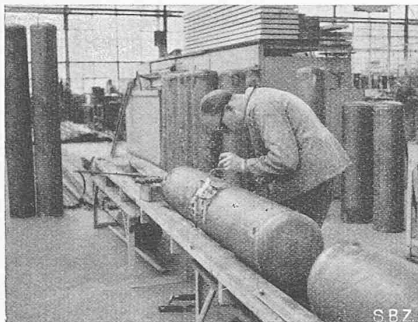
Anschweißen der Flansche für die Ventile auf der Entwicklerkammer
